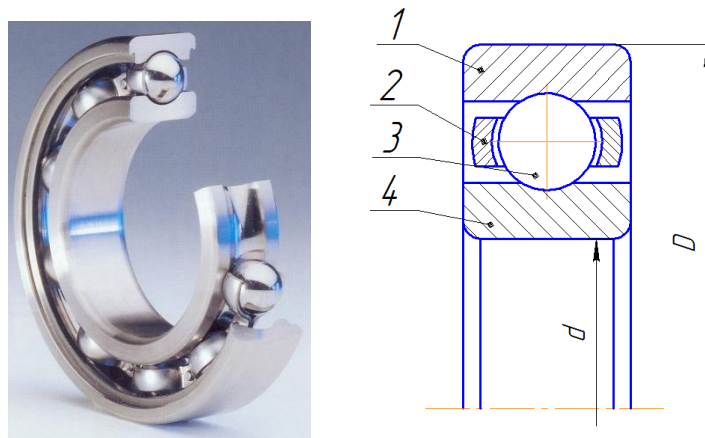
Конструкція кулькового однорядного підшипника:
